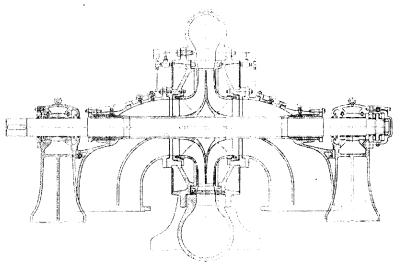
Einstufige Spiralgehäusepumpe mit Leitrad und zweiseitigem Einlauf
